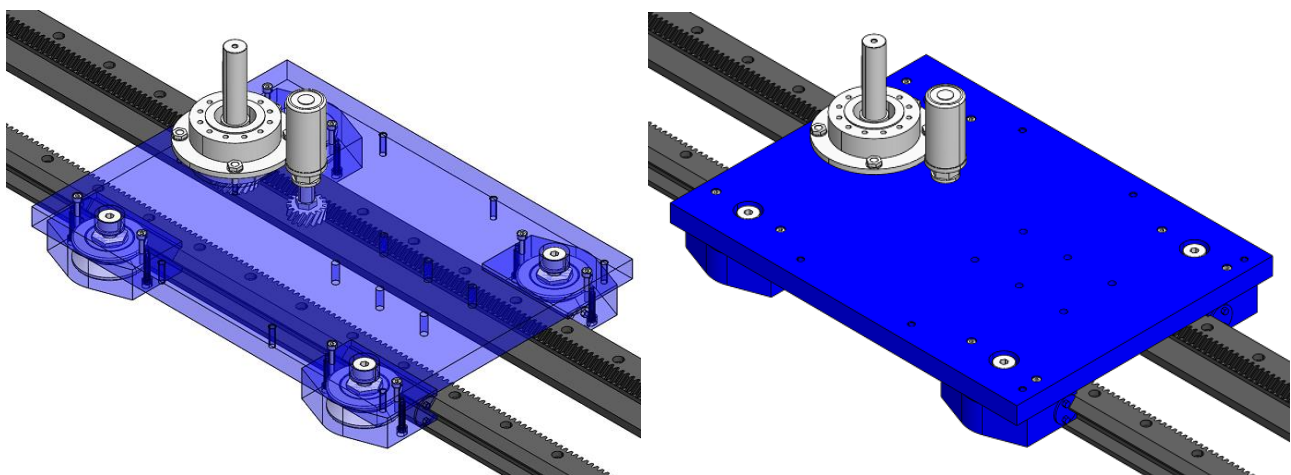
CAD del conjunto ensamblado de los elementos de transmisión de movimiento.
